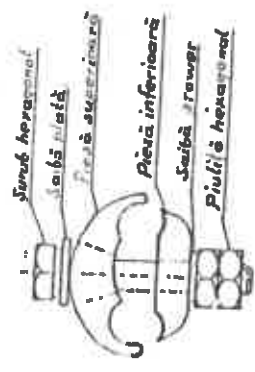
CLEMĂ UNIVERSALĂ U.B.
